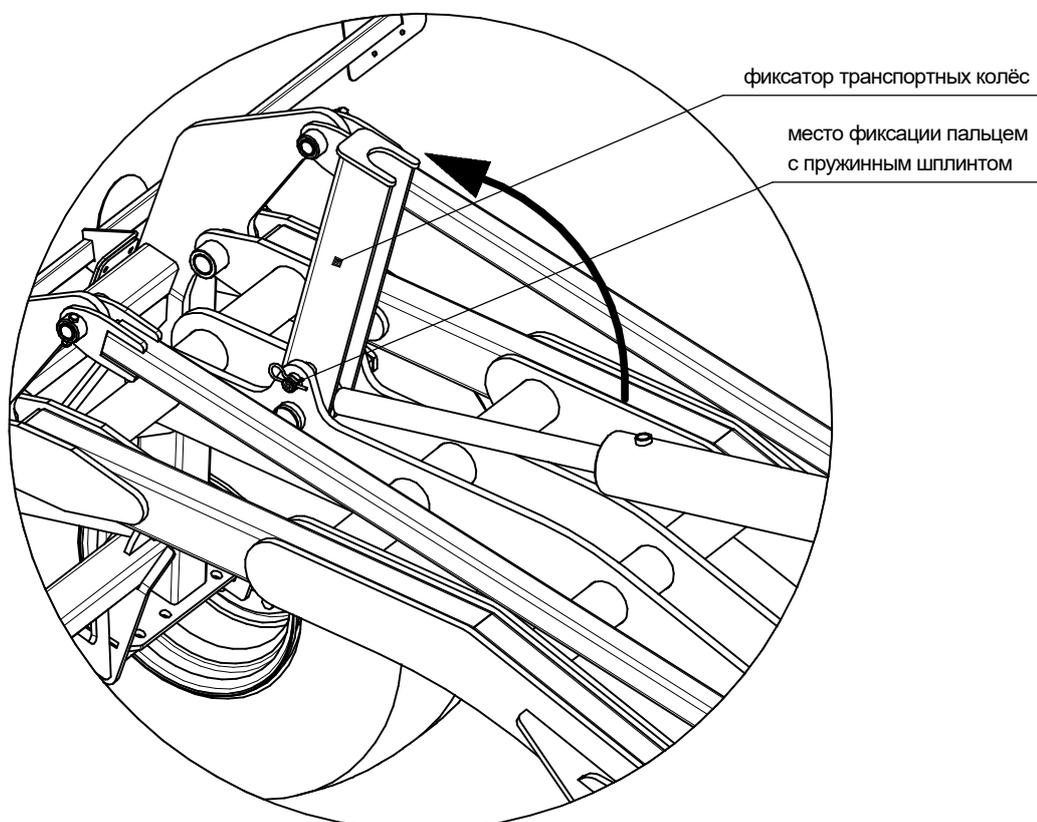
Фиксатор транспортных колёс. Дисковая почвообрабатывающая машина ДПМ "Универсал" / "Универсал Т"
